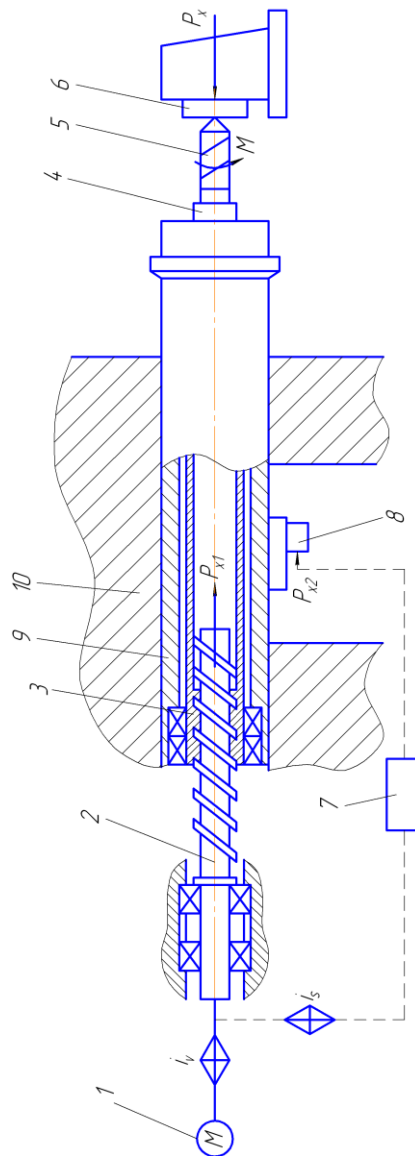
Типова конструкція механізму подач пінольного типу
